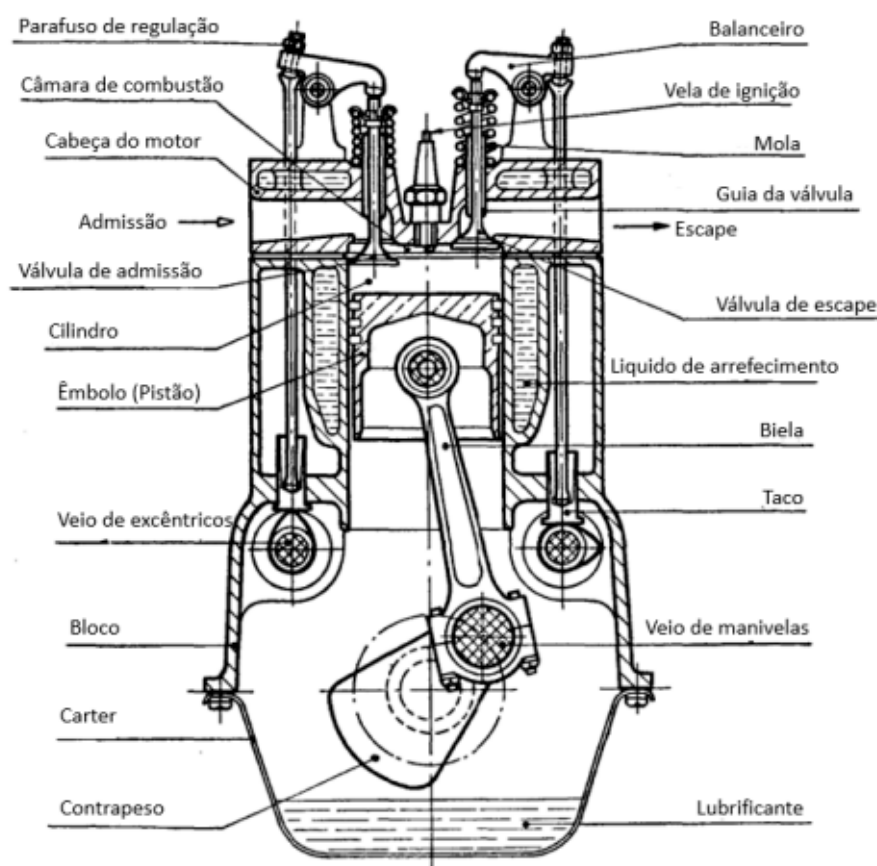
Principais componentes de um motor de combustão interna alternativo [5]
